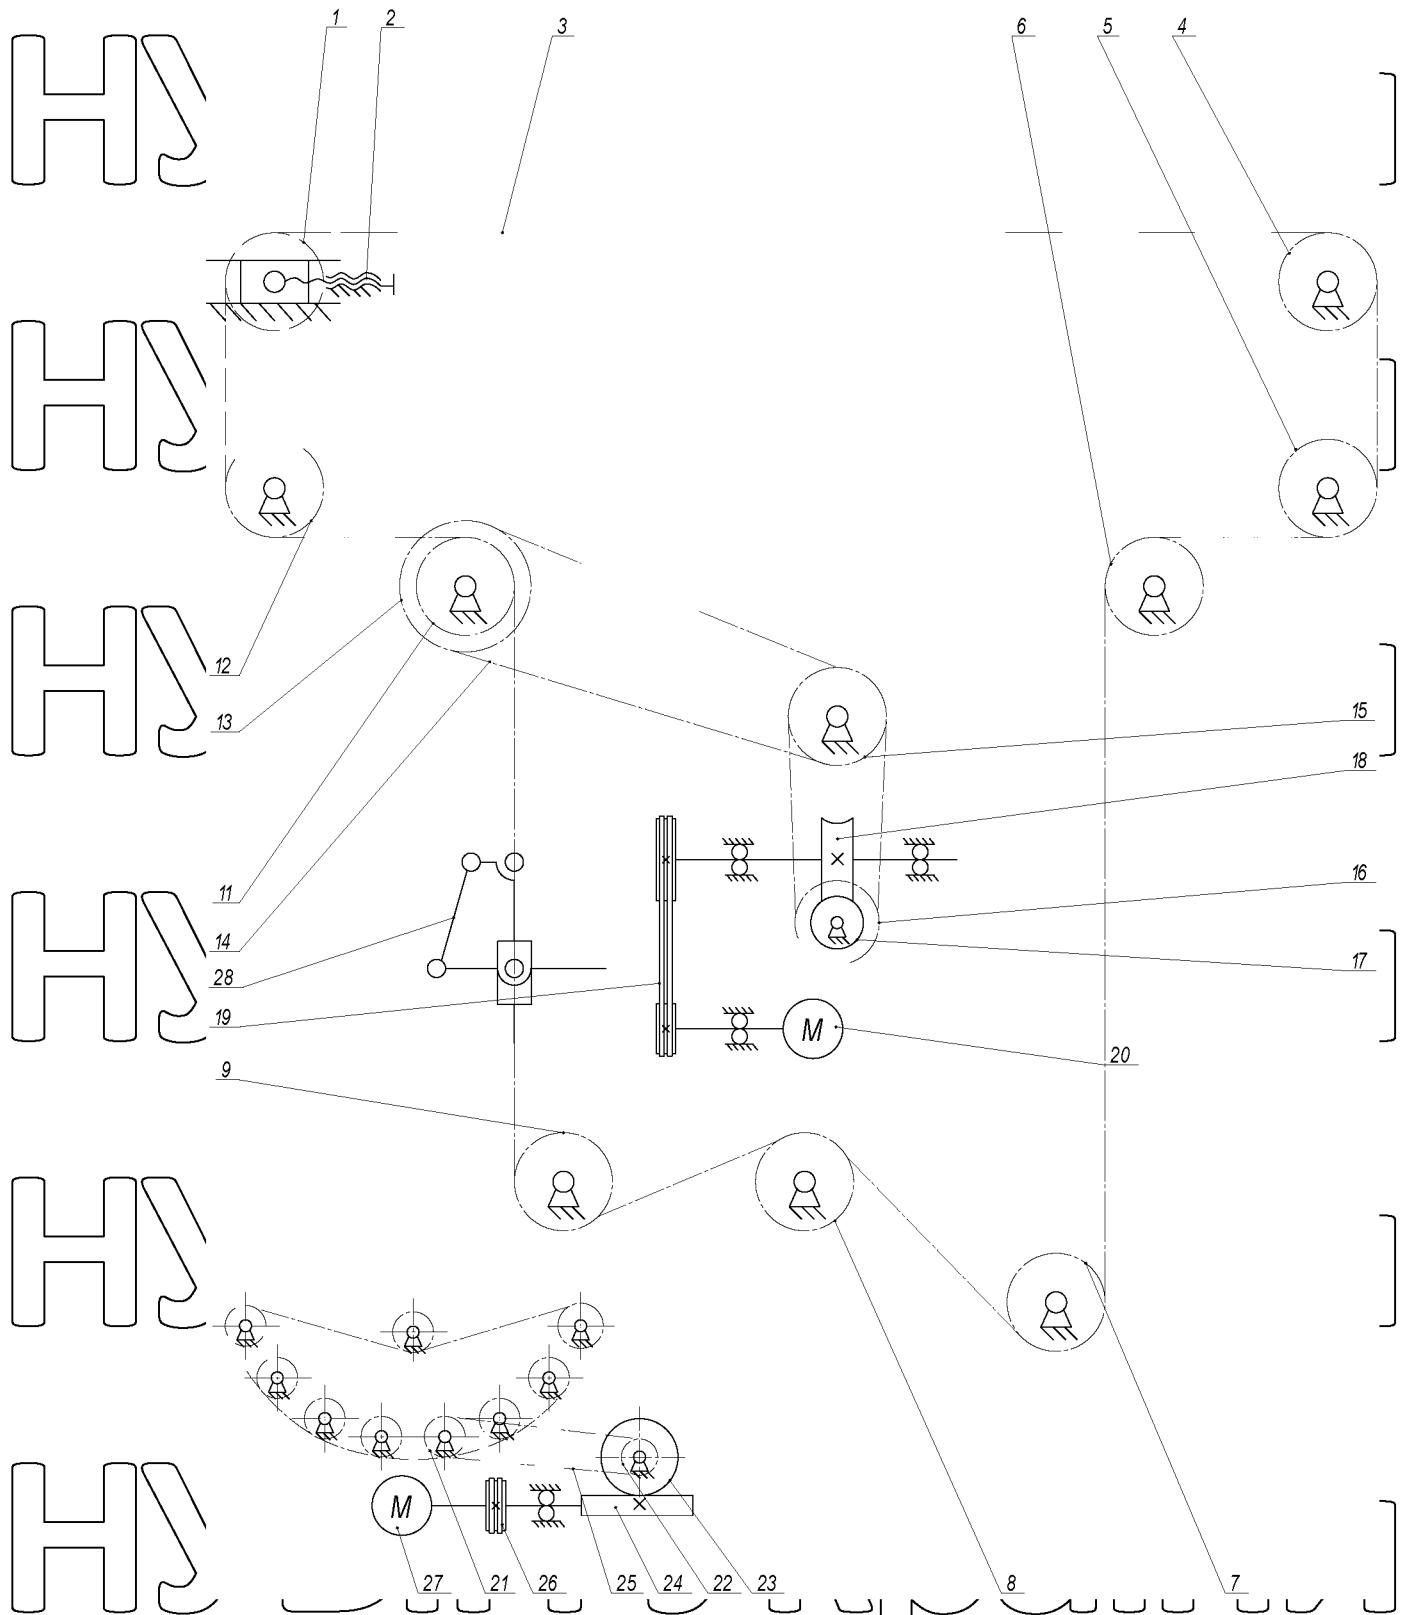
Кінематична схема пристрію для розвантажування
